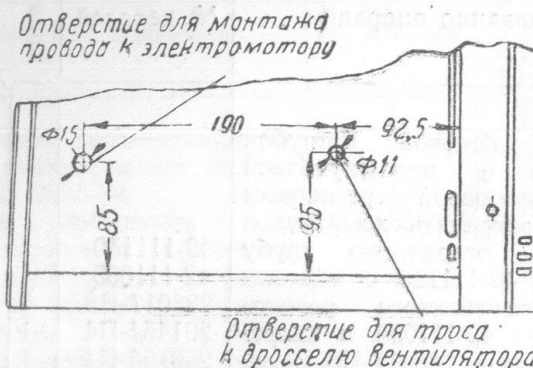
Схема расположения отверстий на правой панели кабины для монтажа провода к электромотору вентилятора и для прохода троса к воздушной заслонке вентилятора
